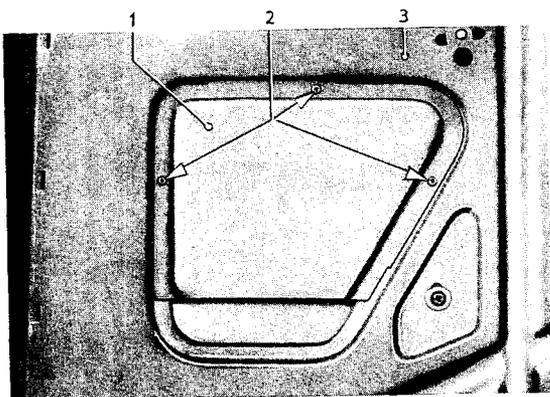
Deckel für hintere Montageöffnung an Türinnenhaut
